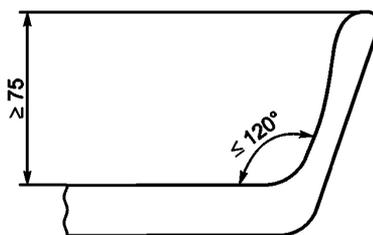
Поперечное сечение опорной поверхности с непрерывной боковой опорой
